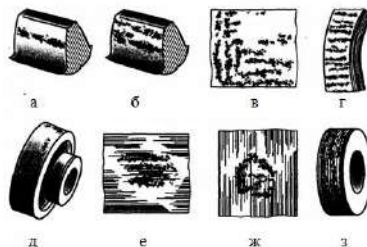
Характерные виды износа поверхностей скольжения: а - выкрашивание; б - отслаивание; в - коррозия; г - эрозия; д - царапины; е - задиры; ж - налипание; з - глубинный вырыв материала и перенос его с другой поверхности трения
